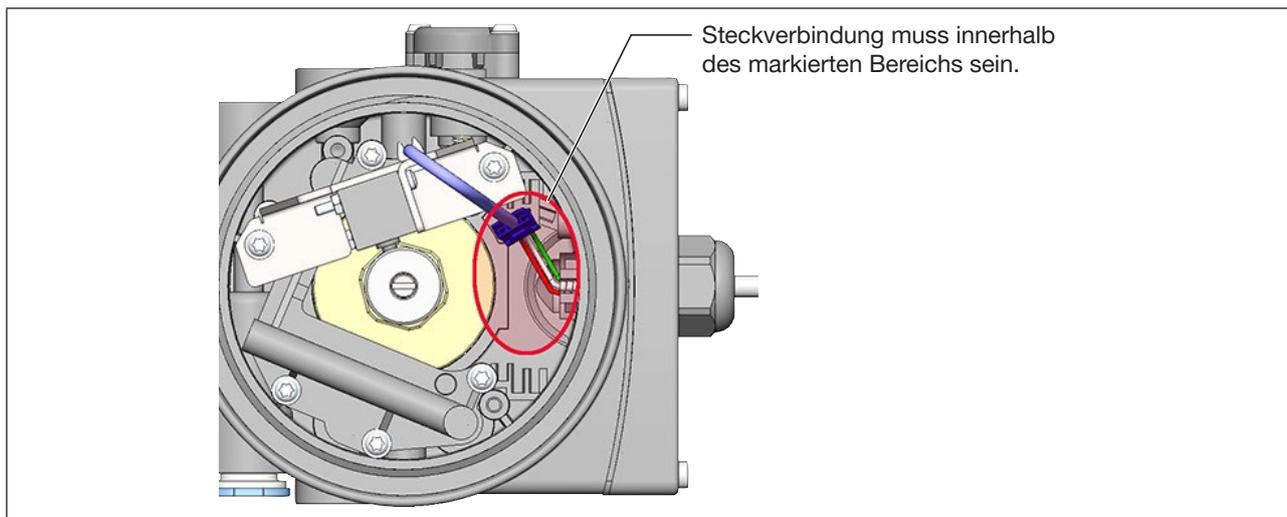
Position der elektrischen Steckverbindung im Wegaufnehmer
